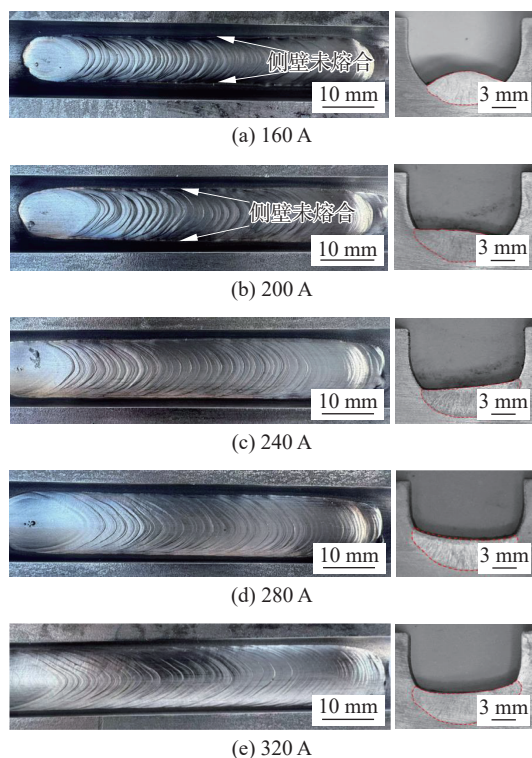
不同焊接电流焊缝表面成形及截面形貌
